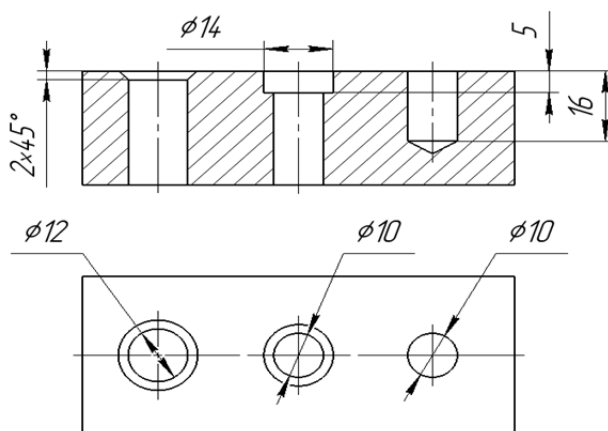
Простановка размеров отверстий на чертеже согласно ГОСТ 2.307–2011
